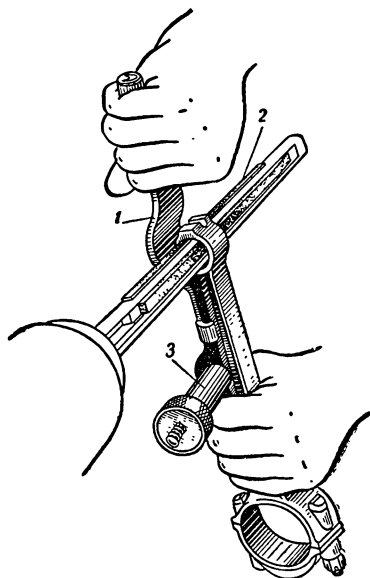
Кондуктор для развертывания отверстия в верхней головке шатуна:
